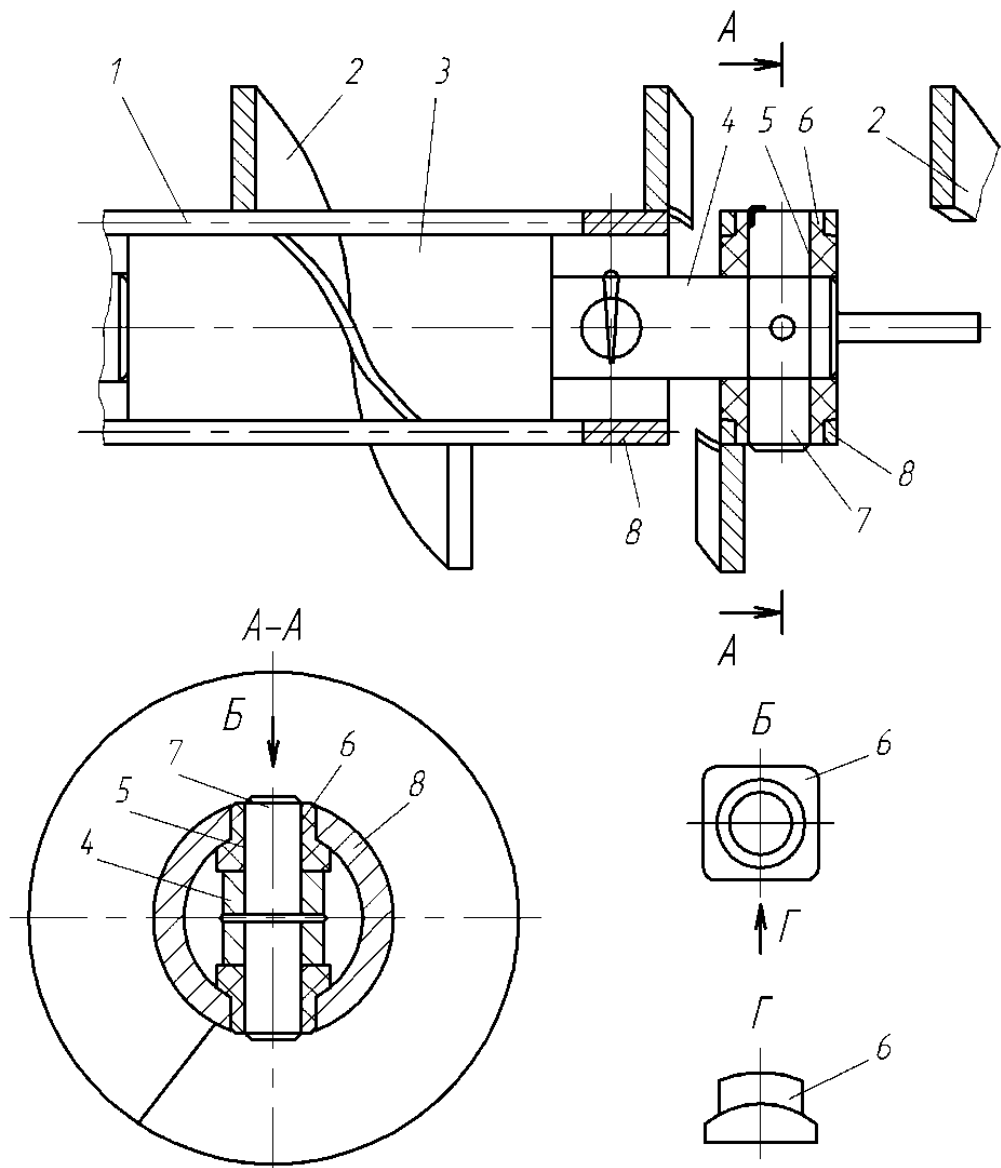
Шарнірний робочий орган гвинтового конвеєра
